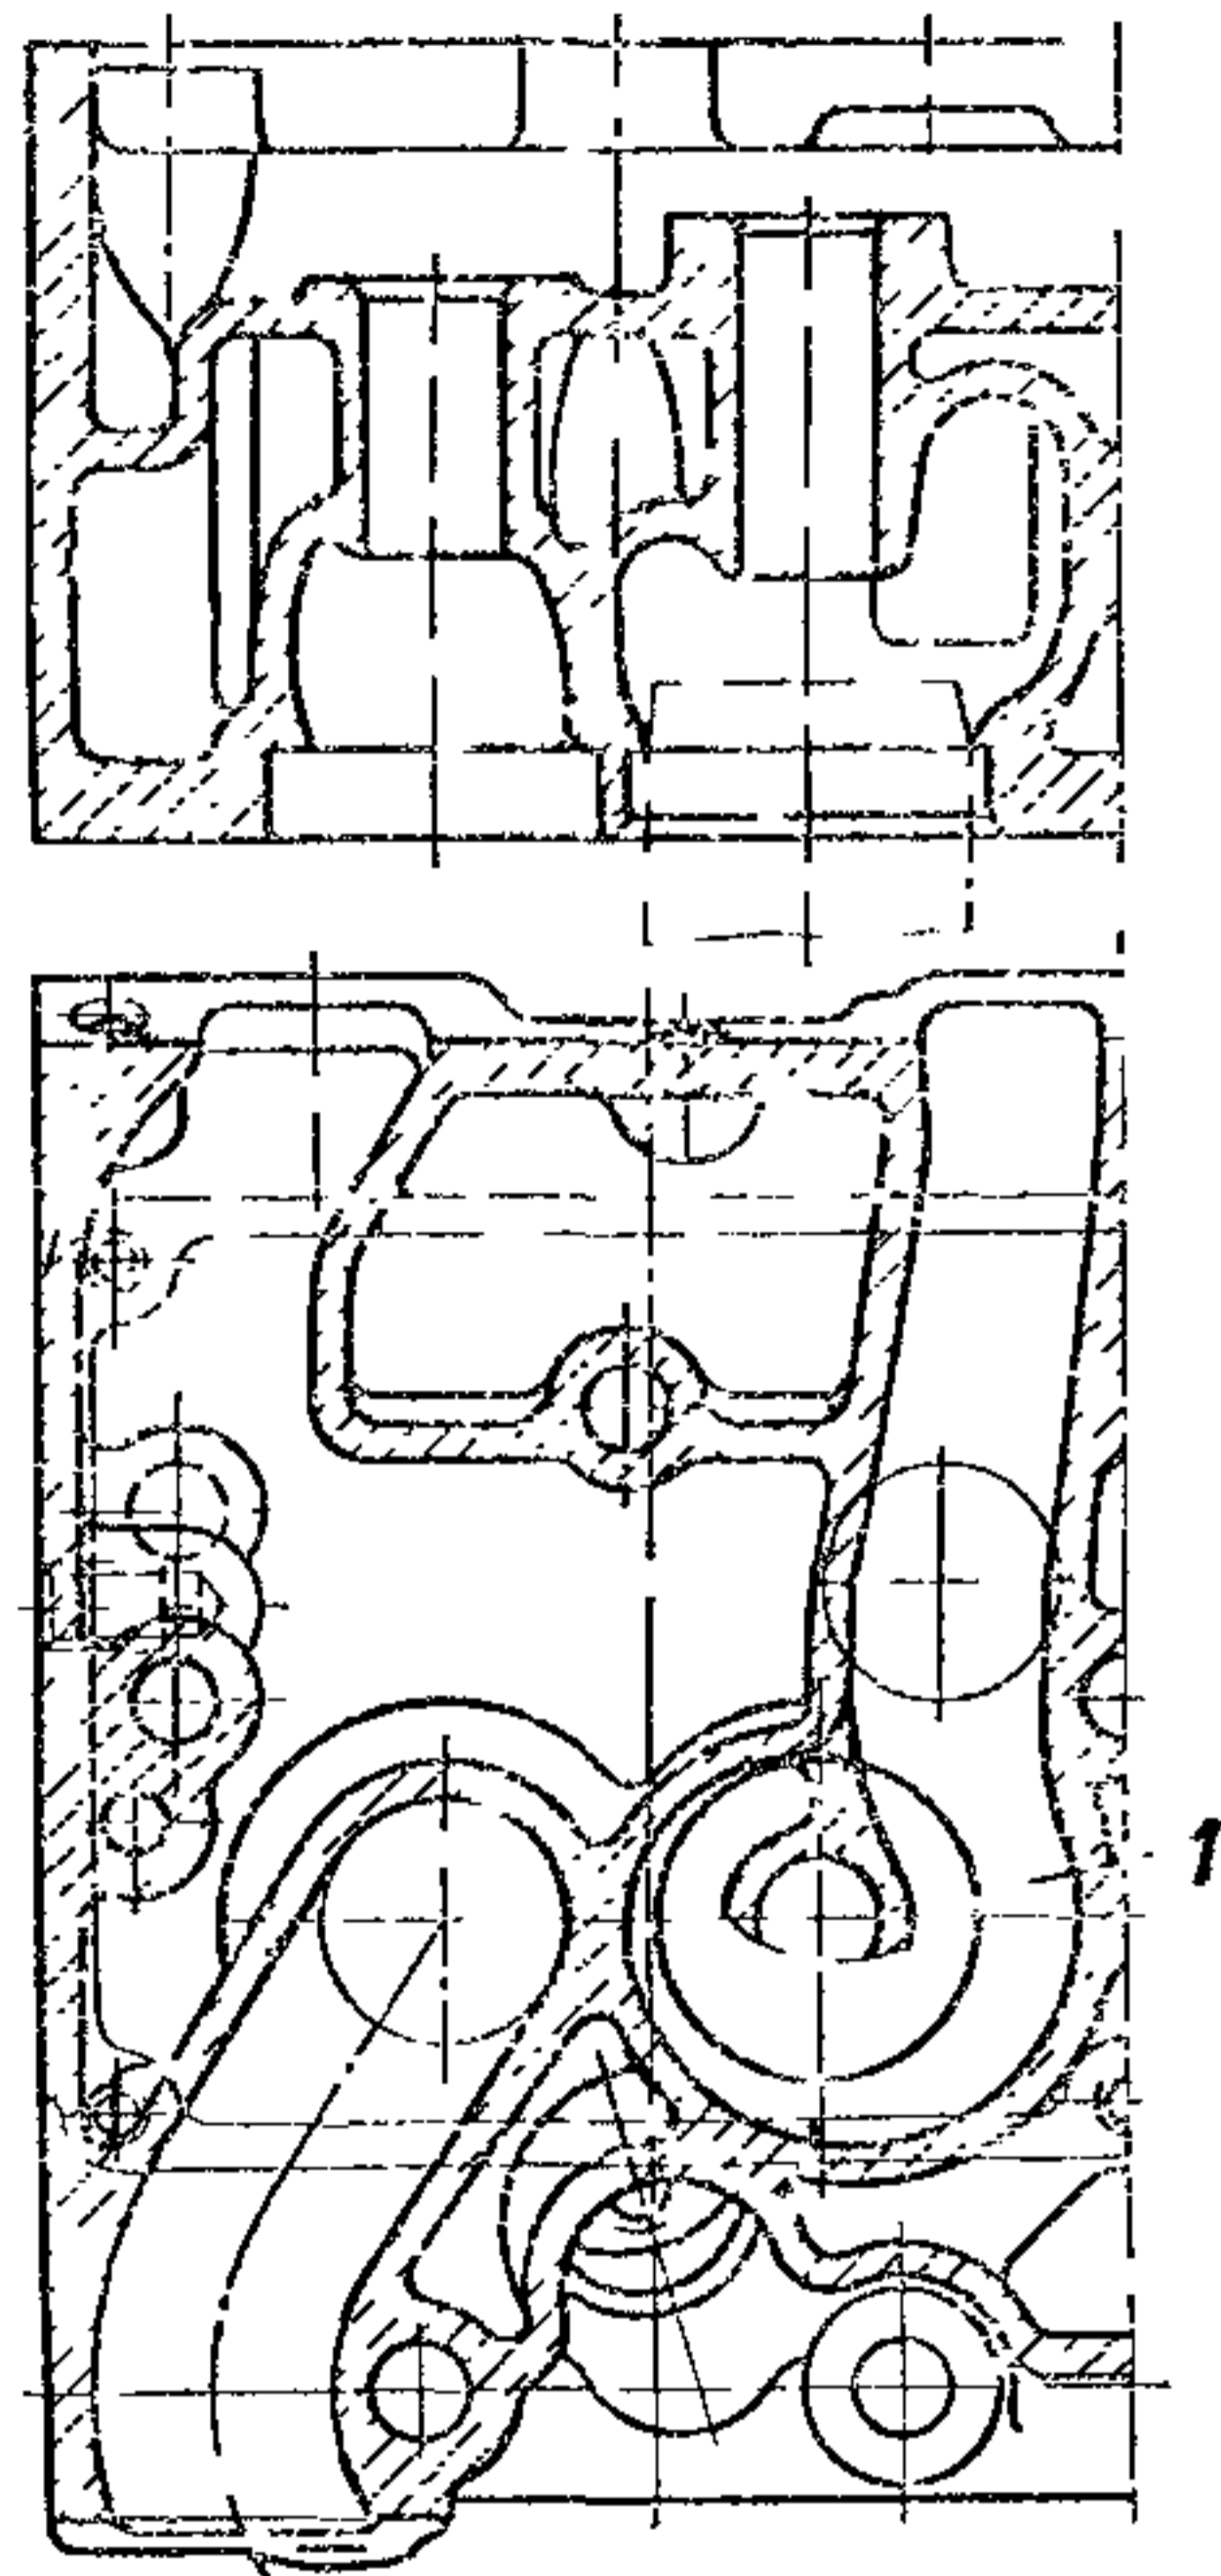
Головка цилиндров бензинового двигателя с винтовым впускным каналом
